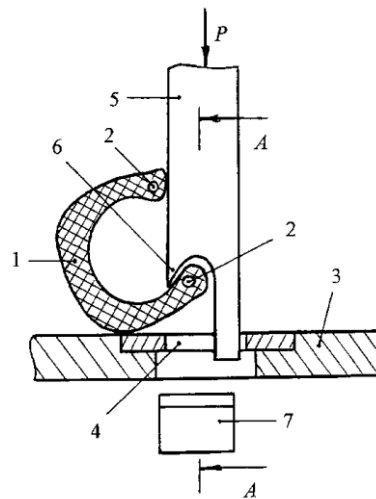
Схема извлечения бортовых колец из автопокрышки [96]
